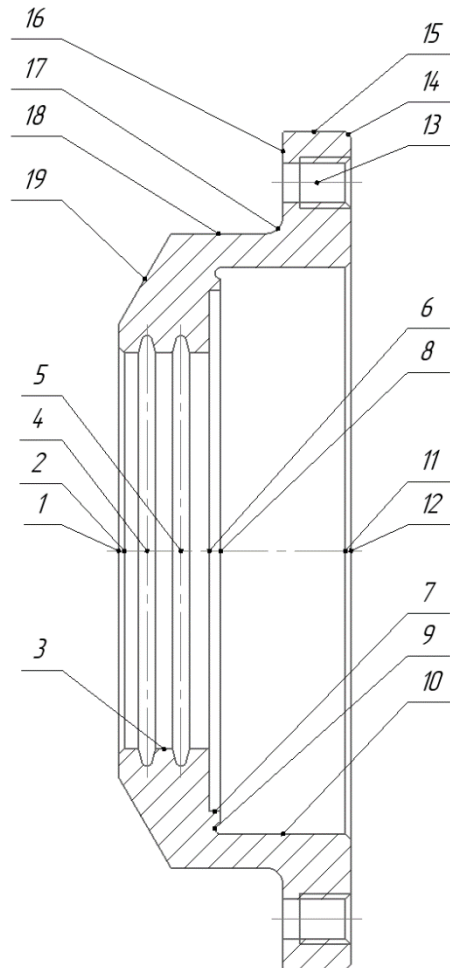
Поверхні деталі «Корпус підшипника 1.1640-2.326.02»
